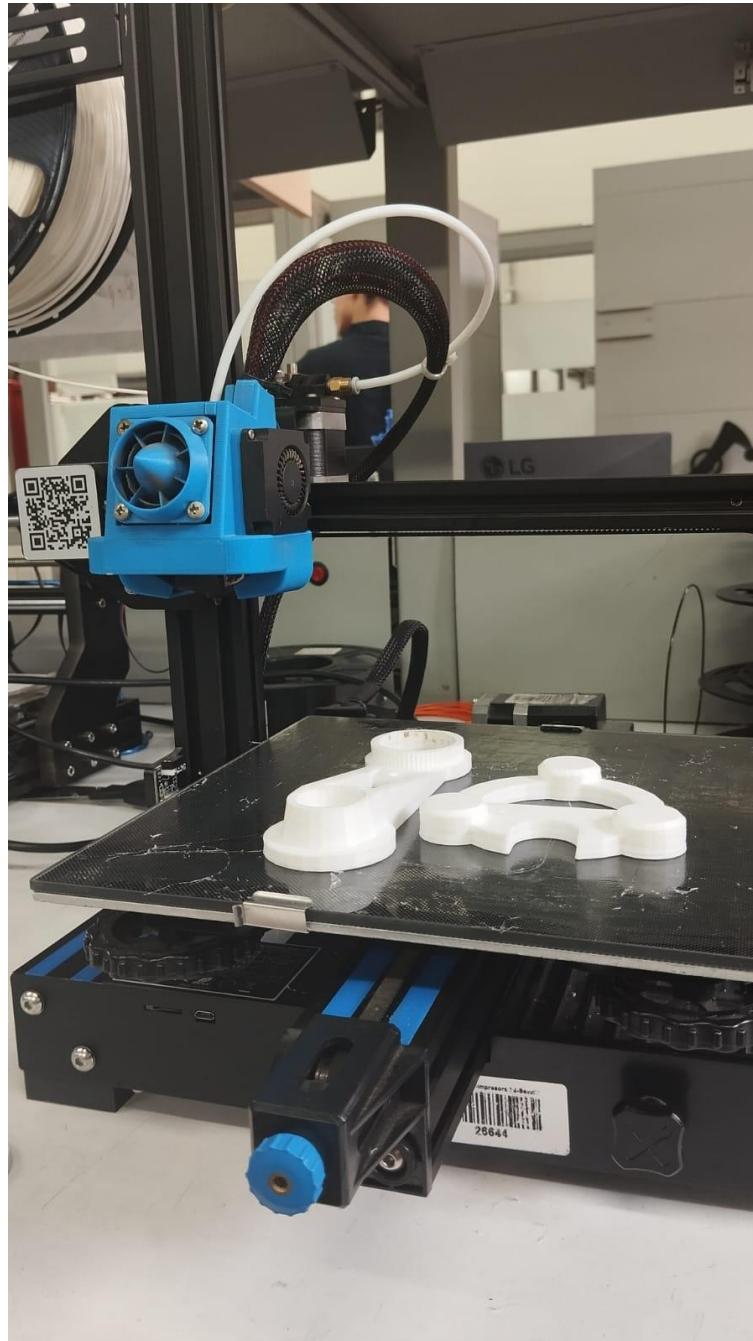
Piezas impresas en PLA sobre la cama de impresión
